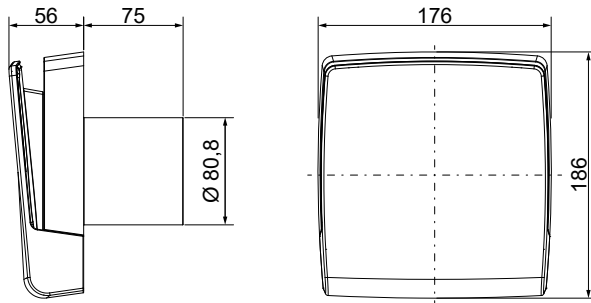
Maßzeichnung – Innenblende Zweitraum
